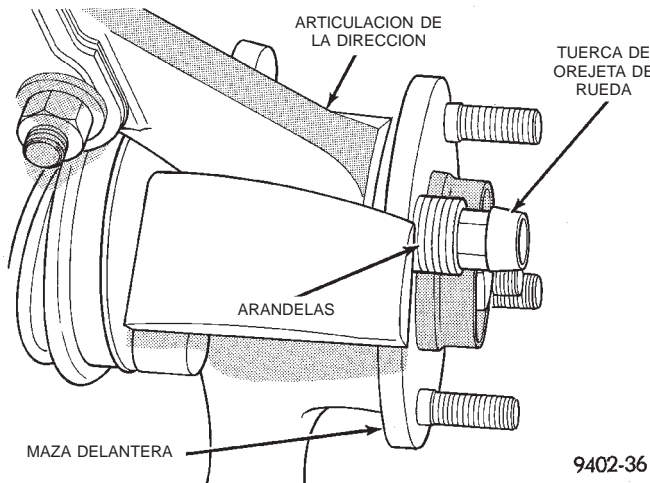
Desmontaje del espárrago de rueda del conjunto de maza y cojinete
